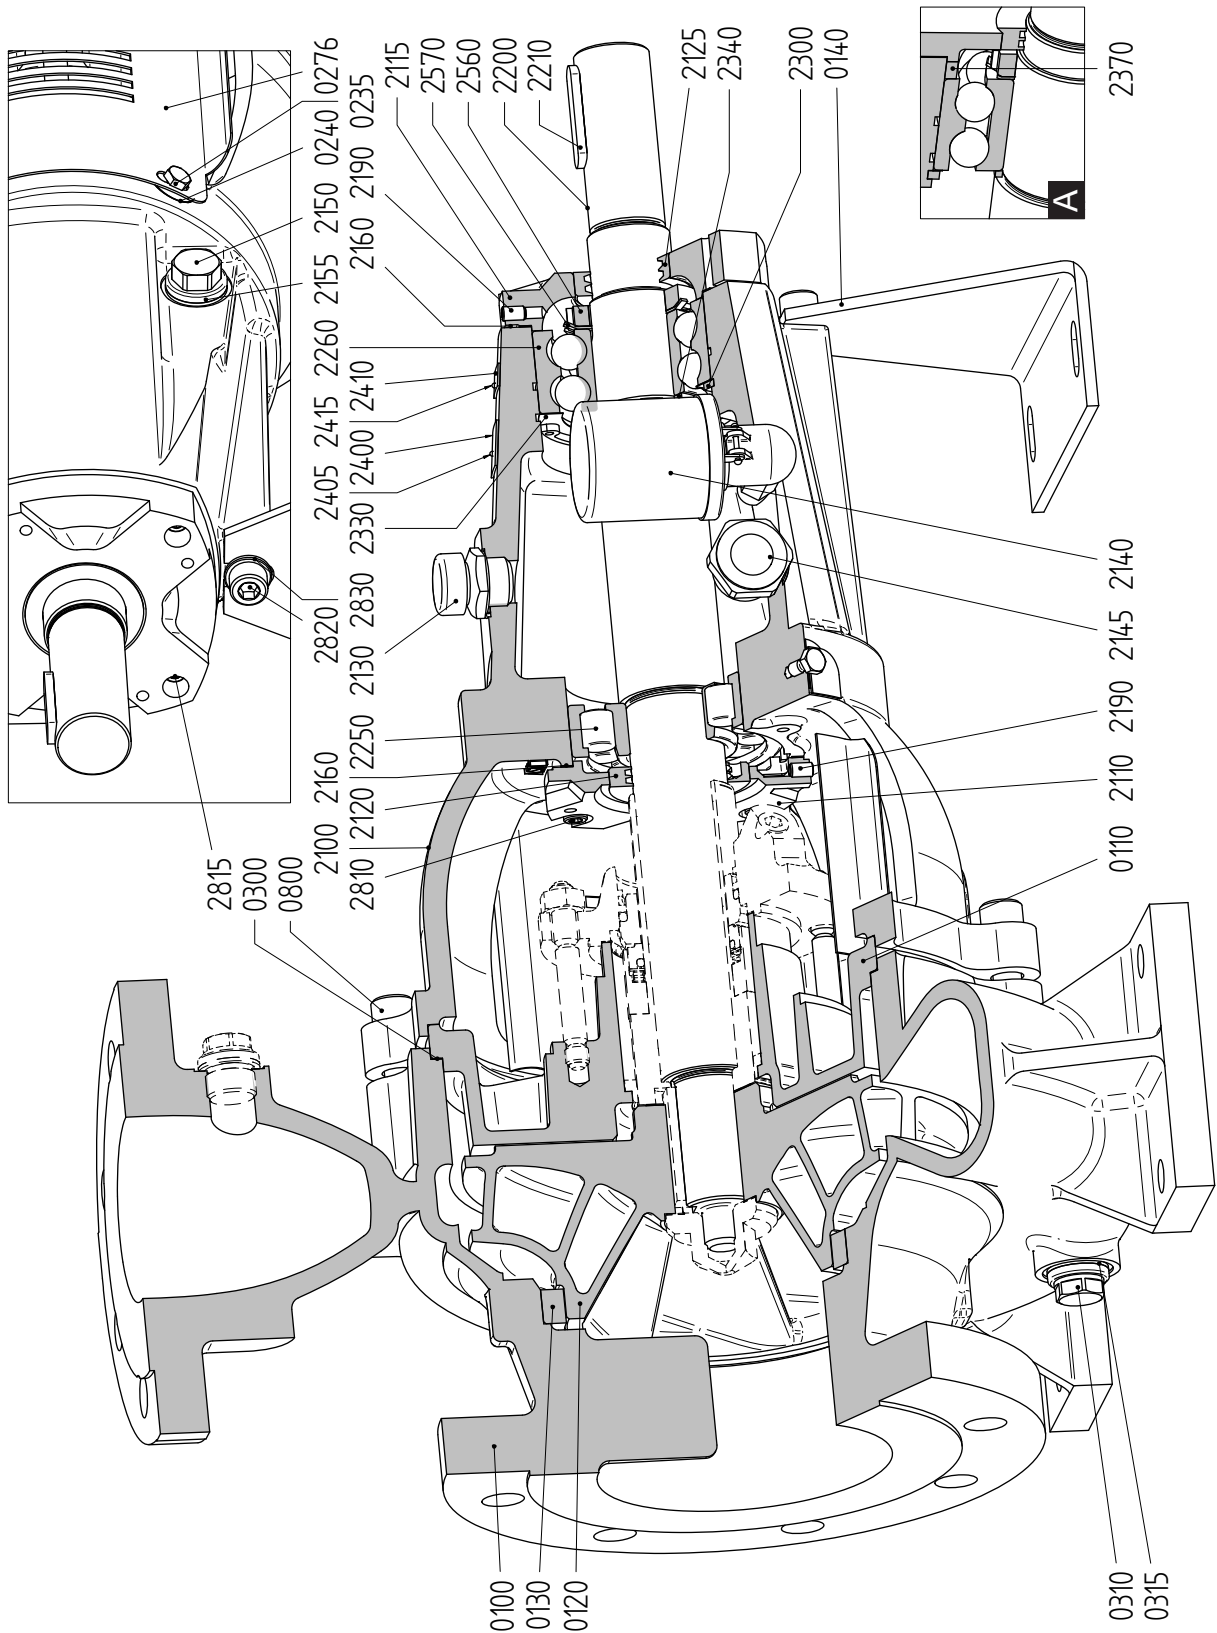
Schéma en coupe L4 (A = groupe de palier 3).
